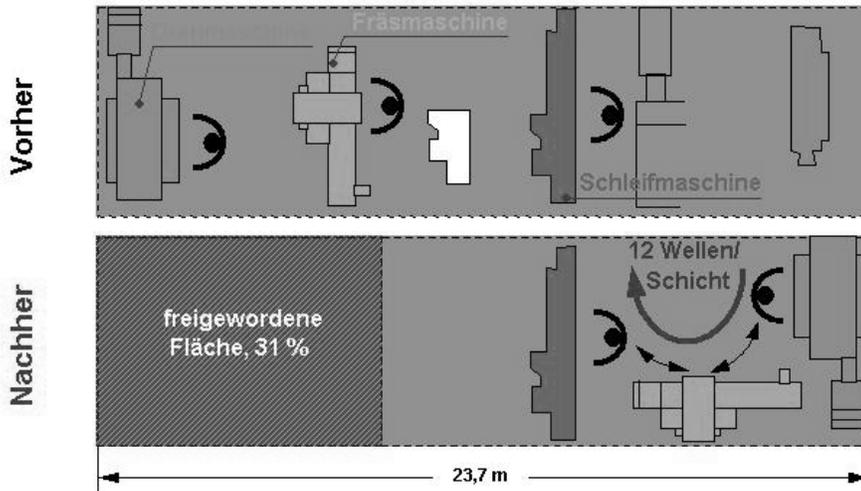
Wellenfertigung in einem Maschinenbauunternehmen, Layout
